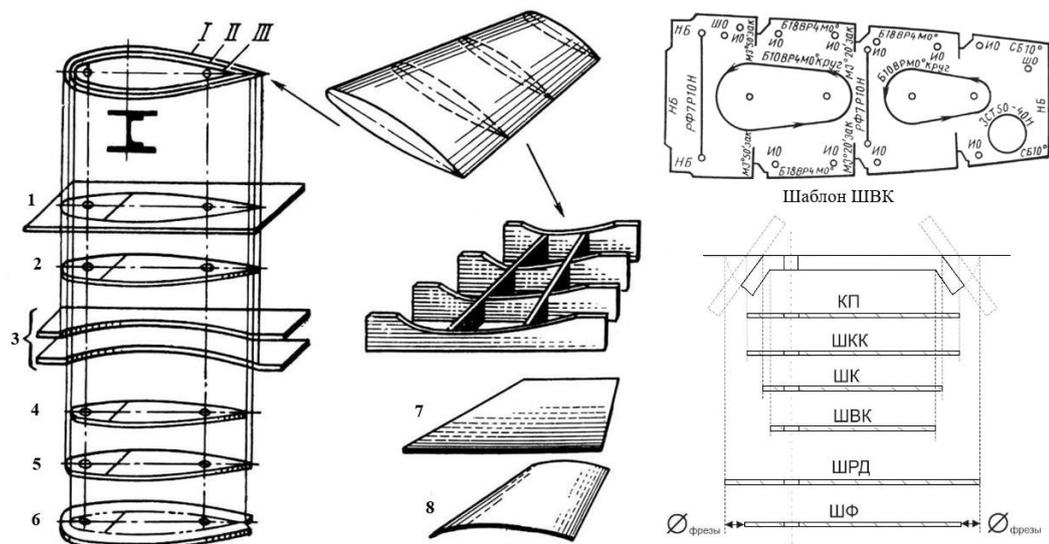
Схема перенесения формы и размеров с теоретического плаза на ШКК и производственные шаблоны: I – теоретический контур сечения поверхности агрегата; II – внешний контур каркаса крыла; III – внутренний контур каркаса; 1 – теоретический плаз; 2 – ШКК; 3 – ШКС поверхности крыла; 4 – ШКС детали каркаса; 5 – ШВК; 6 – ШК; 7 – ШРД; 8 – ШЗ; 9 – ШОК; 10 – КРС
